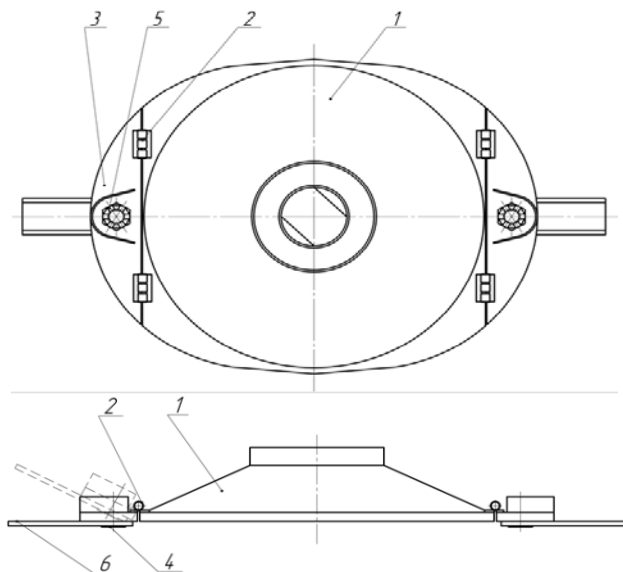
Модернизированный ротор косилки: 1 – центральная часть ротора; 2 – петли; 3 – периферийная часть ротора; 4 – палец; 5 – гайка; 6 – нож
